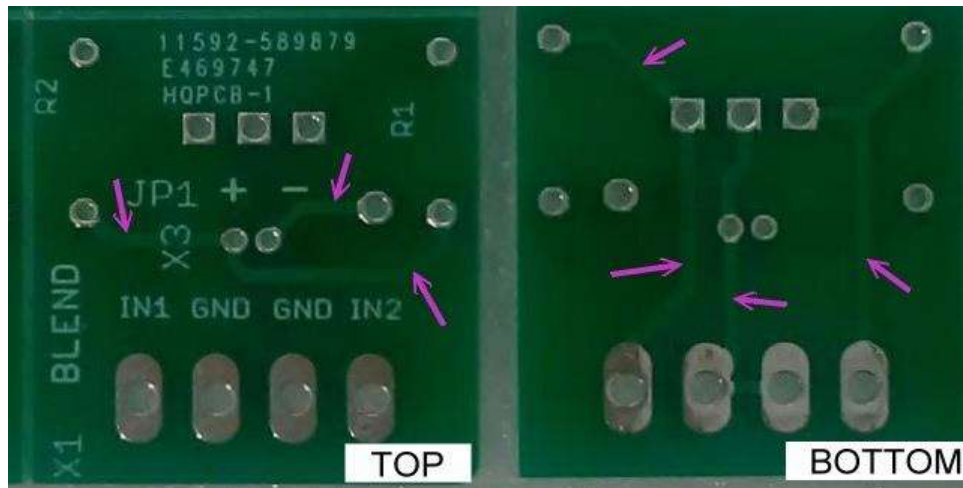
CAPAS TOP Y BOTTOM EN UNA PCB DE 2 CAPAS DE COBRE
